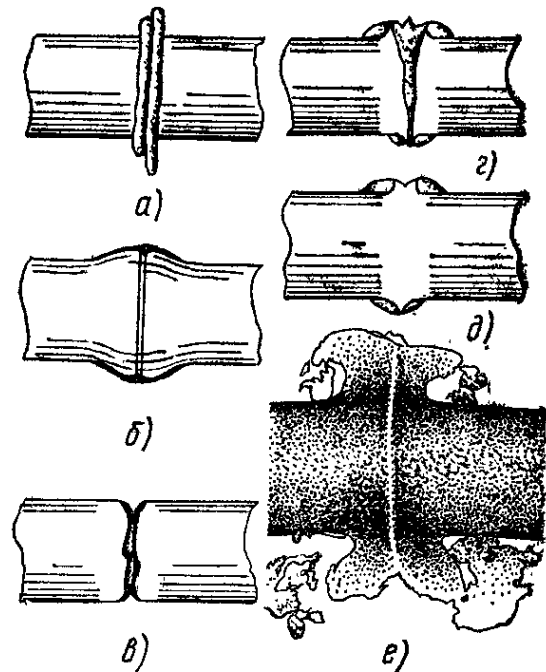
Схемы стыковой сварки сопротивлением (а, б) и оплавлением (в — начальная, г — промежуточная, д — конечная стадии), а также макроструктура стыка, сваренного оплавлением (е)
